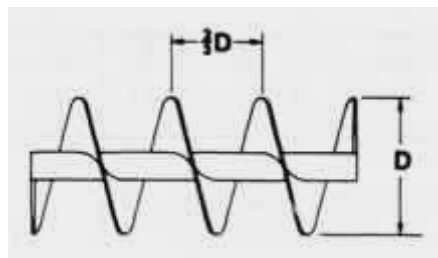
Tornillo de paso corto. Fuente: <http://www.kwsmfg.com/services/screw-conveyor-engineering-guide/conveyor-flight-pitch-types.htm>
